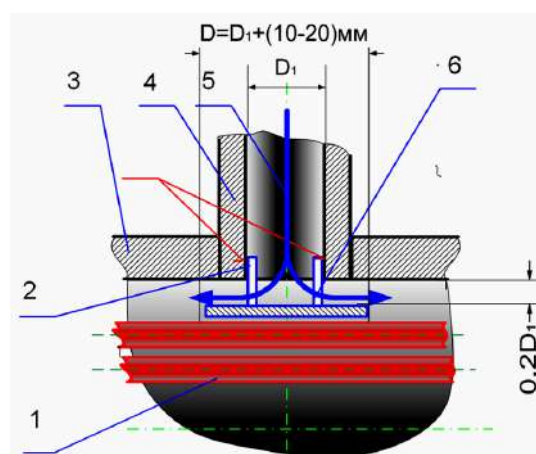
Установка отбойной пластины в корпусе теплообменника
